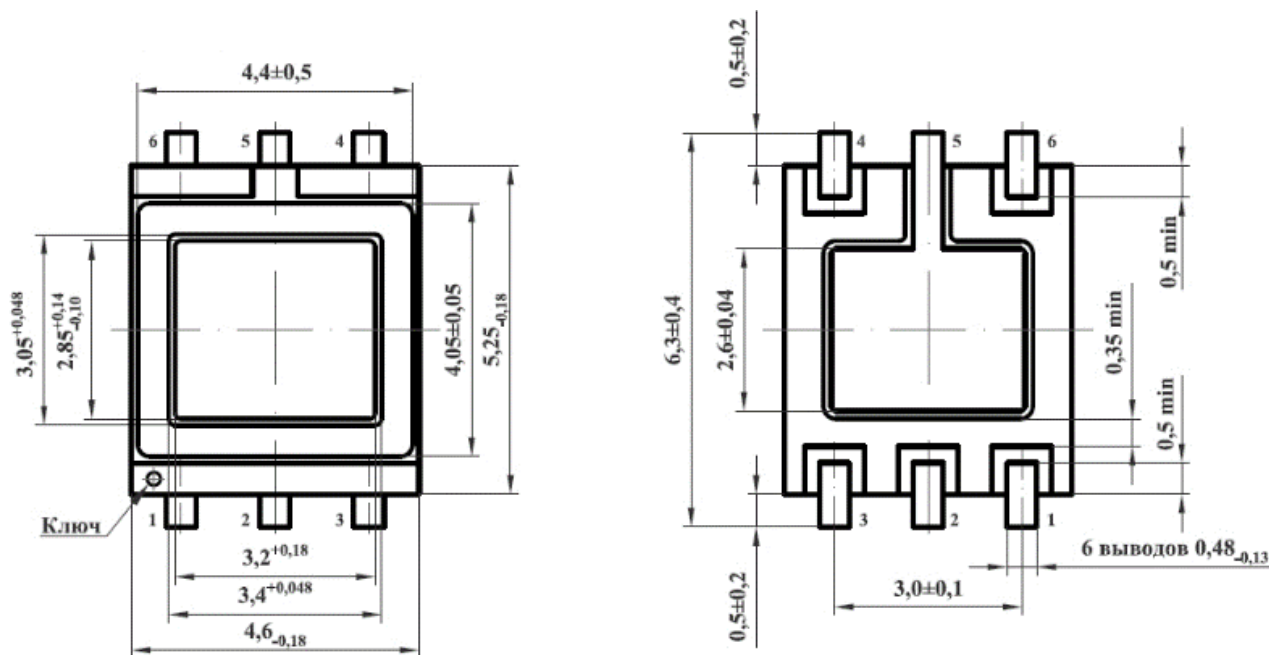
Габаритный чертеж корпуса 5221.6-1 (размеры в мм)
